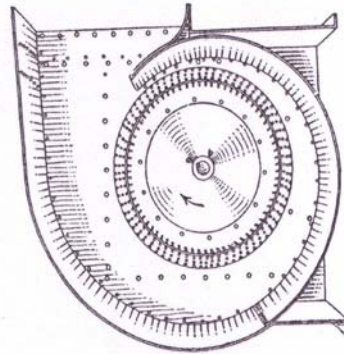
Rodete y caja del ventilador con la tapa desmontada.
